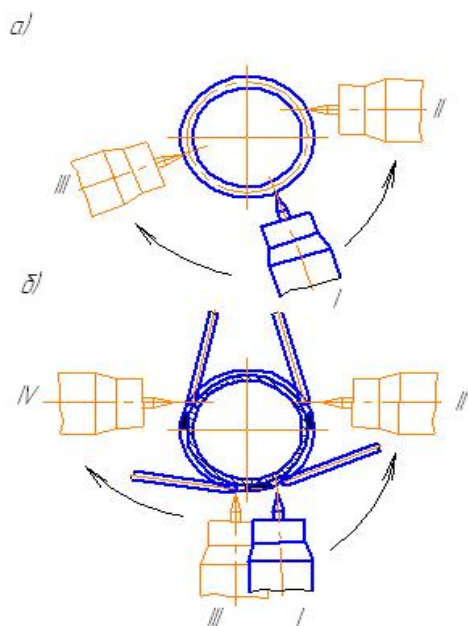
Положение электрода при ручной аргодуговой сварке неповоротных стыков труб: а) сварка без присадки; б) сварка с присадкой
